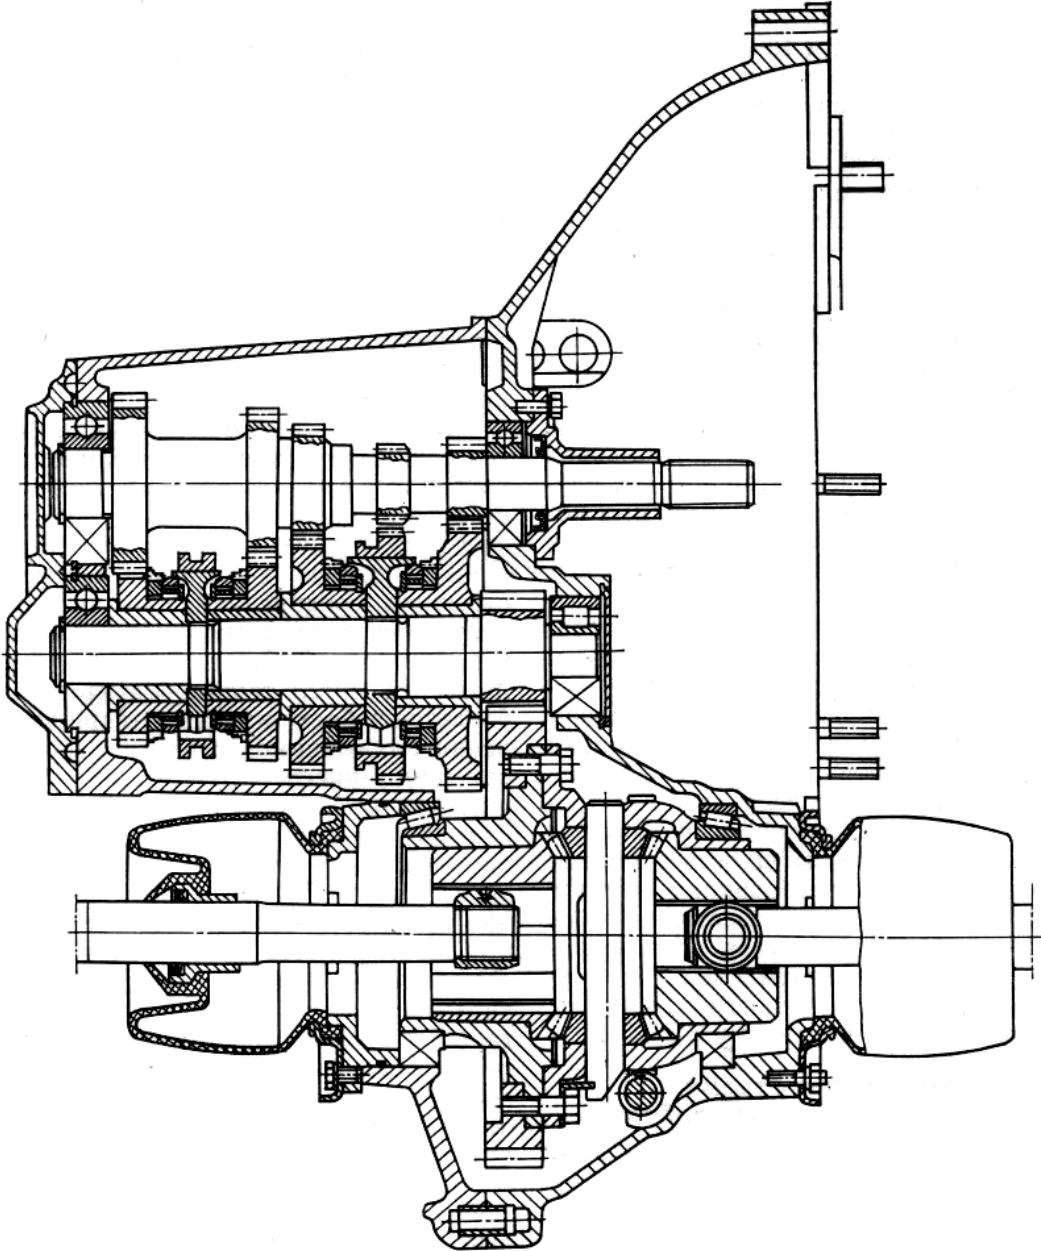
Конструкция коробки передач переднеприводного автомобиля с поперечным расположением двигателя
